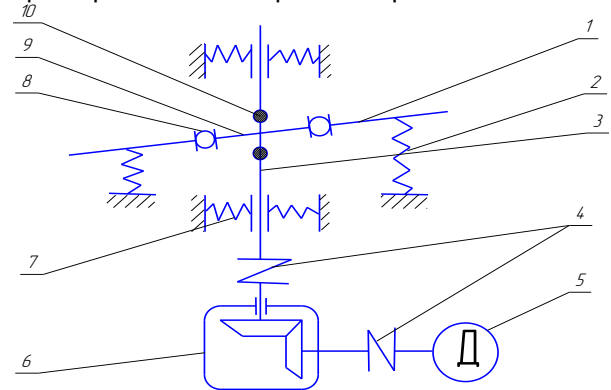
Схема вібропривода грохоту: 1 – віброплатформа; 2, 7 – пружні елементи; 3 – вал; 4 – муфта; 5 – електродвигун; 6 – конічний редуктор; 8 – підшипниковий вузол; 9 – втулка; 10 – противага.
